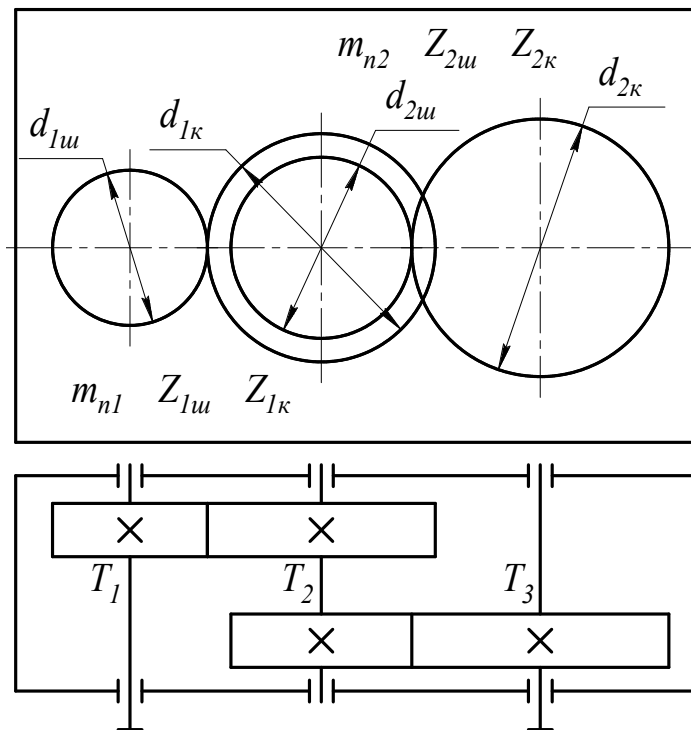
Кинематическая схема и условные обозначения двухступенчатого цилиндрического редуктора
